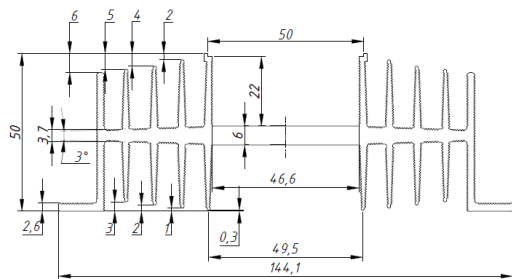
габаритные и установочные размеры радиатора РТР061.1
